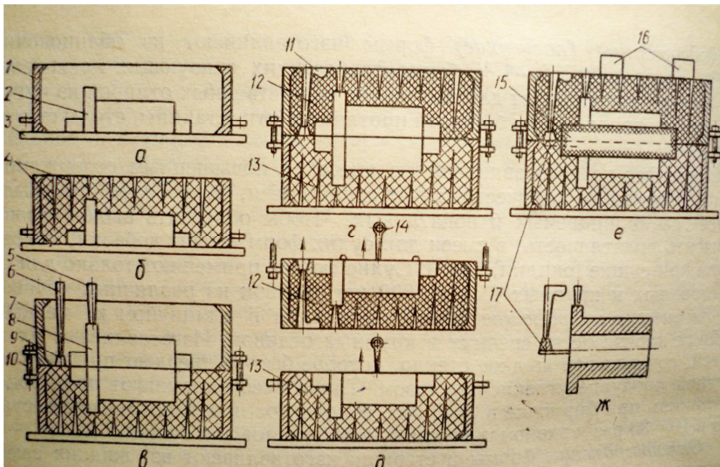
Виготовлення чавунної заготовки способом лиття у піщану форму
